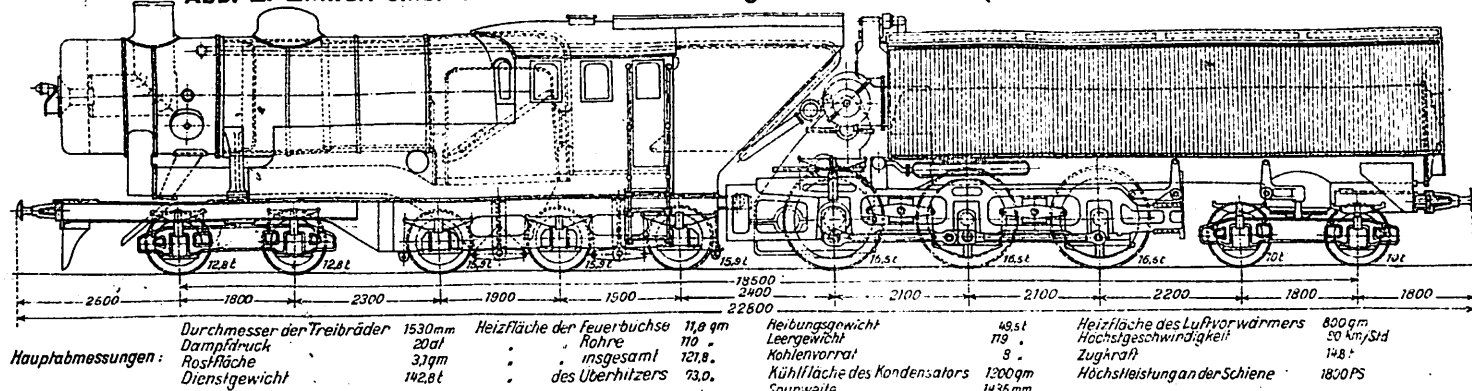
Entwurf einer Turbinenlokomotive für England.
